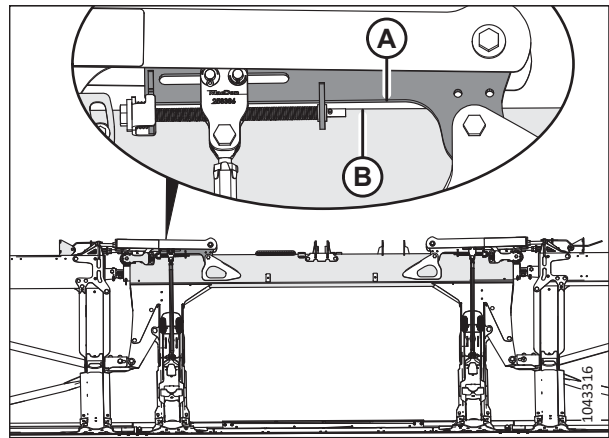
Parallélisme du levier coudé et du tube arrière
